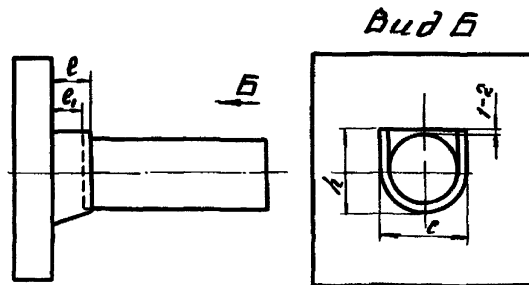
Тавровое соединение одинарных стержней с пластиной, выполняемое дуговой одноэлектродной сваркой в медных формах.
